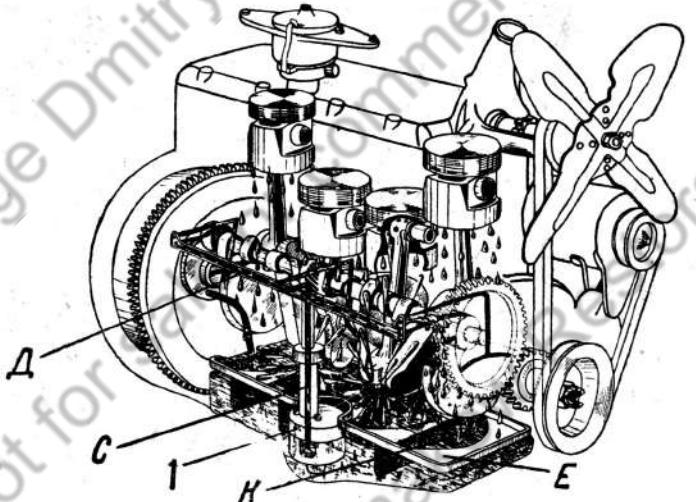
Схема смазки двигателя М: 1 — масляный насос; С — вертикальный масляный канал; Д — горизонтальный масляный канал; Е — поддон; К — корытце
